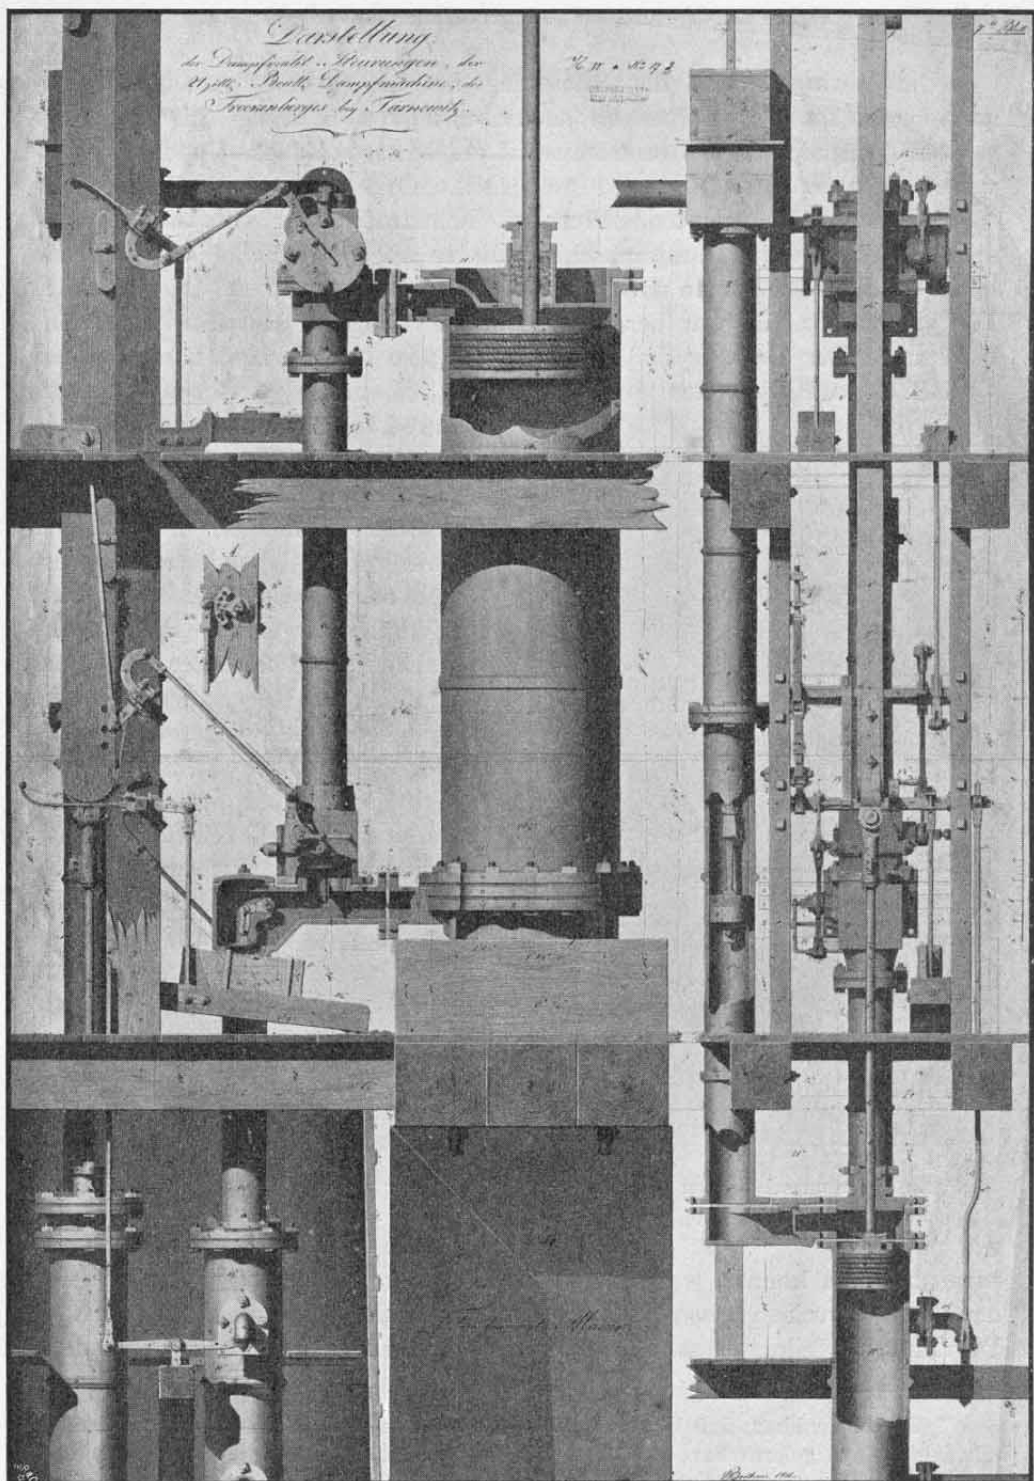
Zylinder und Steuerung einer von Holtzhausen 1805 erbauten Wasserhaltung.
